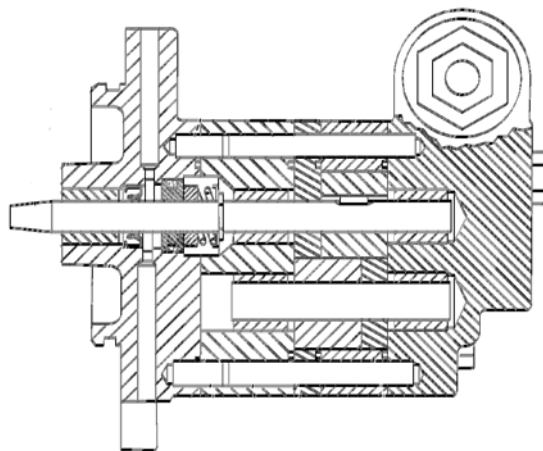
Шестеренний масляний насос двигуна Cummins
